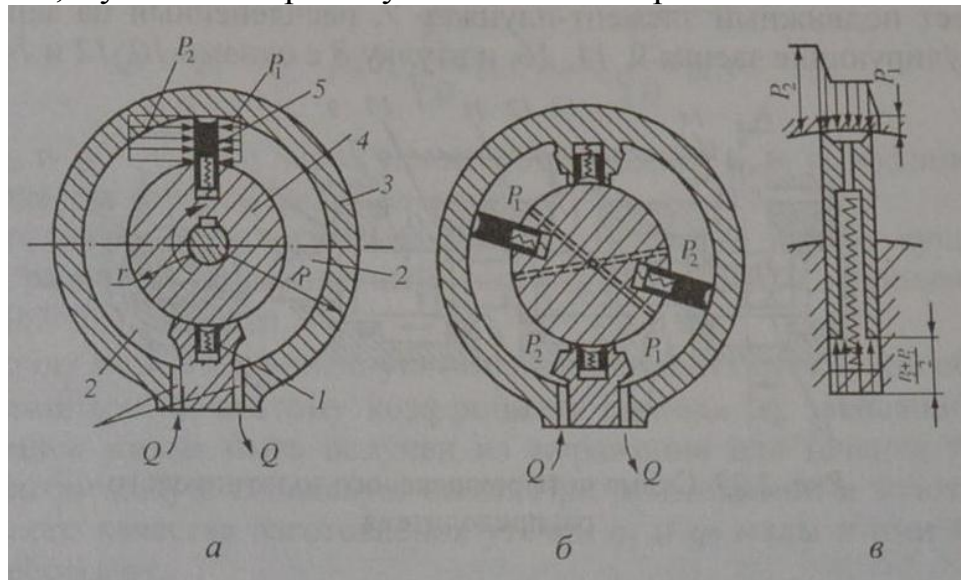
Поворотные гидродвигатели: а - двухкамерный; б - четырехкамерный; в - гидростатически разгруженная пластина
